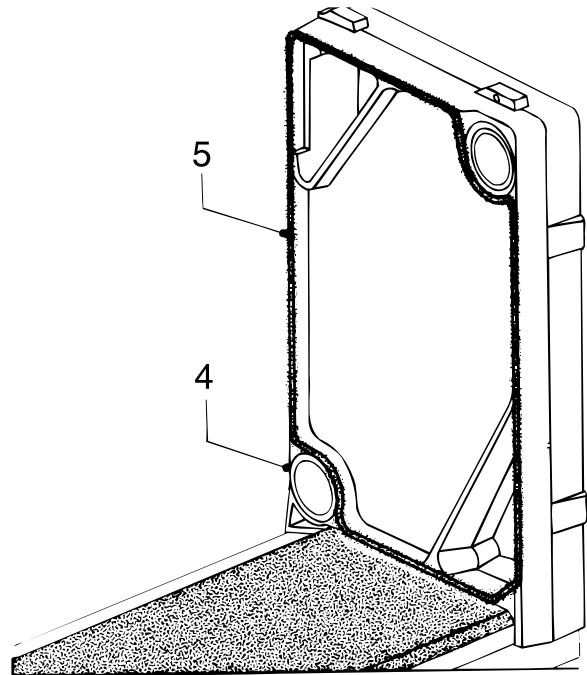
Weiße Dichtschnur (6) \varnothing 8mm für innen einlegen.
